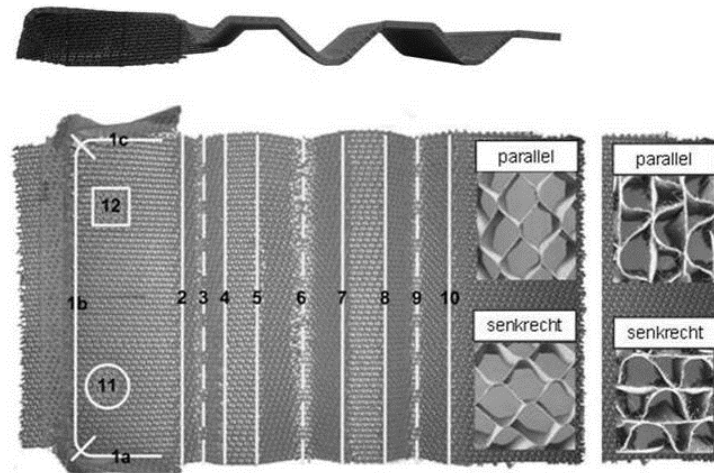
Umformzonen einer Papierwabe umgeformt mit Werkzeug
